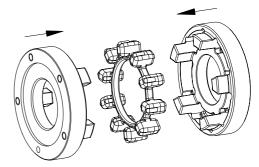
Montaggio della flangia di guida con anello in elastomero
